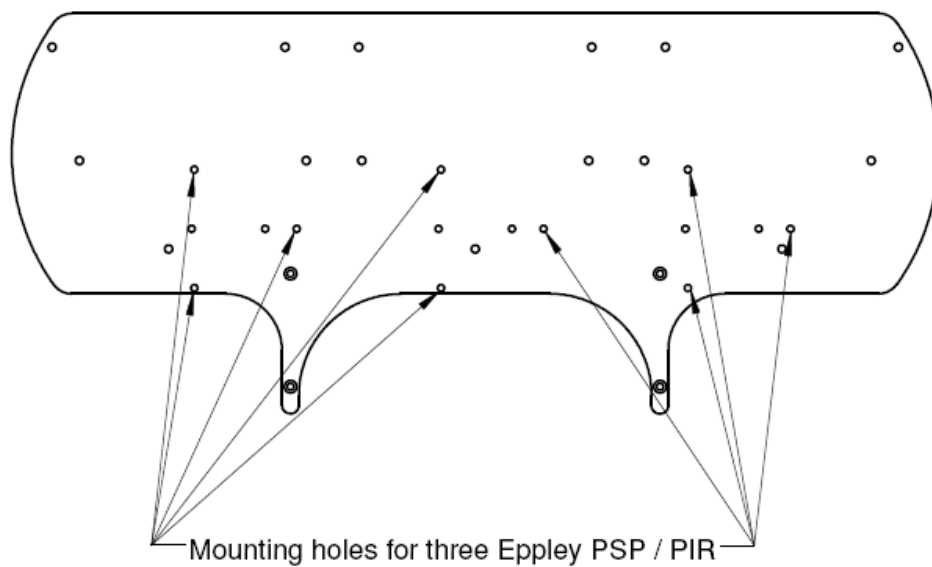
B Montaje de radiómetros Eppley en el Plato de montaje superior
